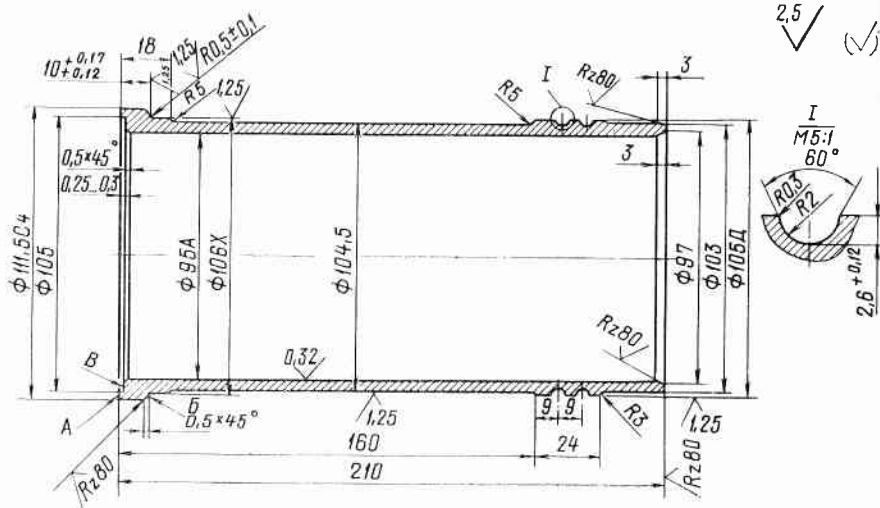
Втулка цилиндра — 7Д6—13.00.03 Fig. 70. Cylinder liner, 7Д6—13.00.03
